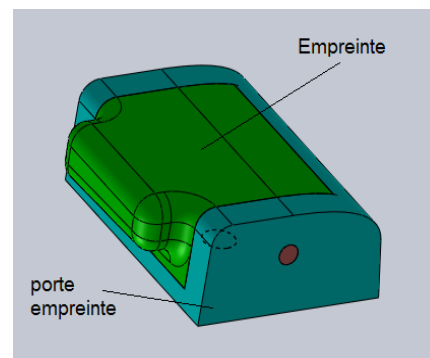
Pièce du coin réalisée par Solidworks.
